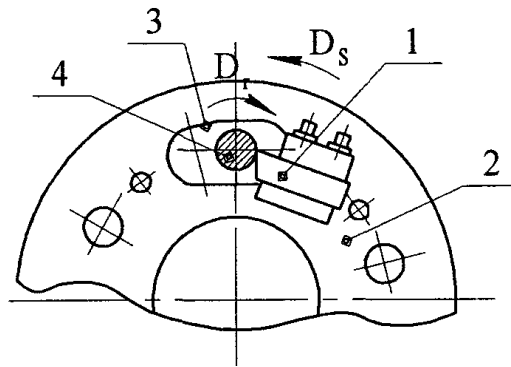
Схема відрізки деталі на верстаті з револьверною голівкою, вісь якої паралельна осі шпинделя: 1 - відрізний різець; 2 - револьверна голівка; 3 - паз, 4 - заготованка
